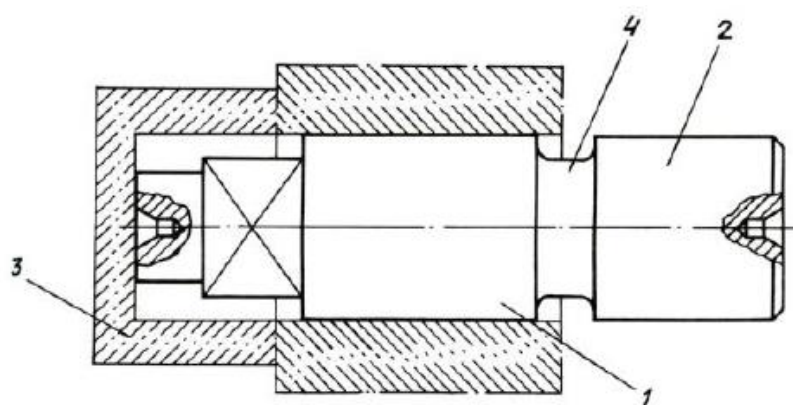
Схема придания заготовке фиксированного по длине оправки положения:
